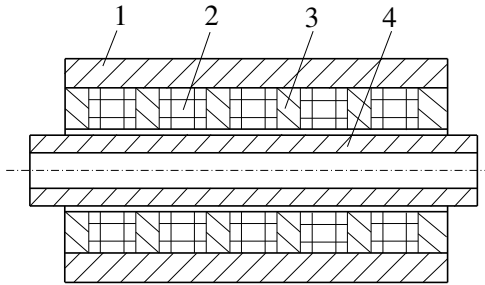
Цилиндрический (коаксиальный) линейный двигатель: 1 – индуктор двигателя; 2 – обмотки индуктора; 3 – металлические шайбы; 4 – вторичный элемент
